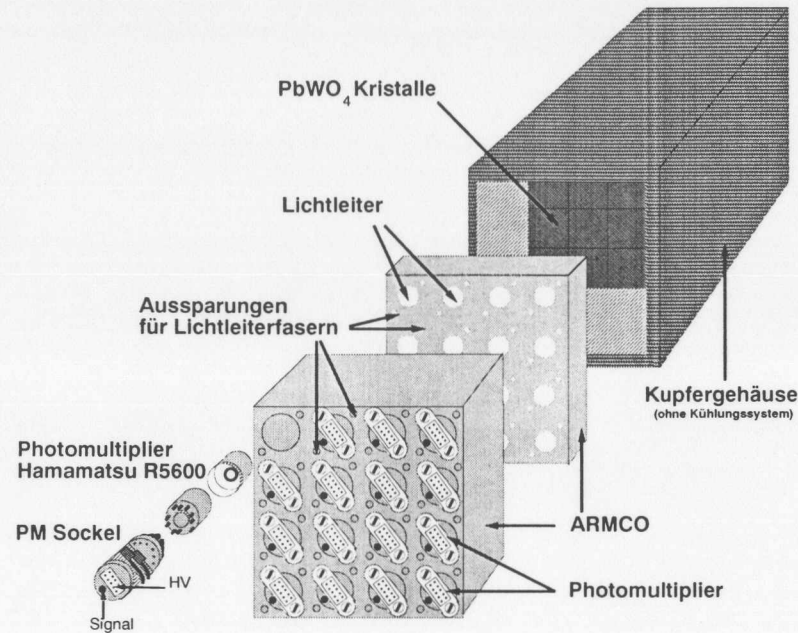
Explosionszeichnung des 3. BPC-Prototyps: Das endgültige BPC III unterscheidet sich in Details teilweise ein wenig von der in der Zeichnung dargestellten Ausführung. Im Text wird auf die Unterschiede eingegangen.
